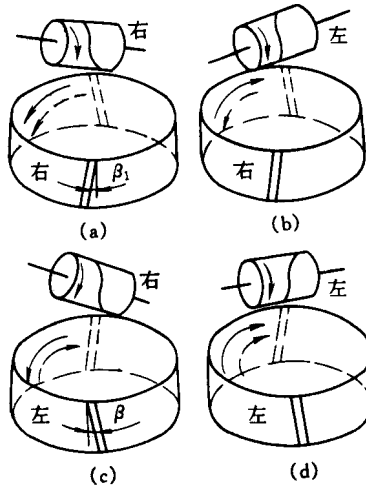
滚齿机加工斜齿圆柱齿轮
